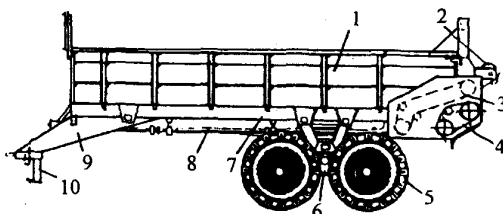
Схема типовой машины для внесения твёрдых органических удобрений: 1 – кузов; 2 – разбрасывающее устройство; 3 – привод рабочих органов; 4 – привод транспортёра; 5 – колесо; 6 – баланси́р; 7 – рама; 8 – трансмиссия; 9 – дышло; 10 – опора.
